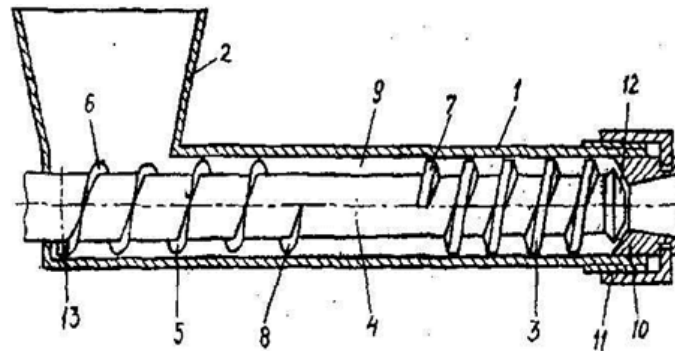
Экструдер для приготовления кормовой массы из измельчённой соломы: 1 - корпус; 2 - загрузочный бункер; 3 - прессующий шнек; 4 - хвостовик; 5 - подающий шнек; 6 - задний виток подающего шнека; 7 - задний виток прессующего шнека; 8 - передний виток подающего шнека; 9 - камера; 10 - втулка; 11 - гайка; 12 - коническая головка; 13 - гильза
